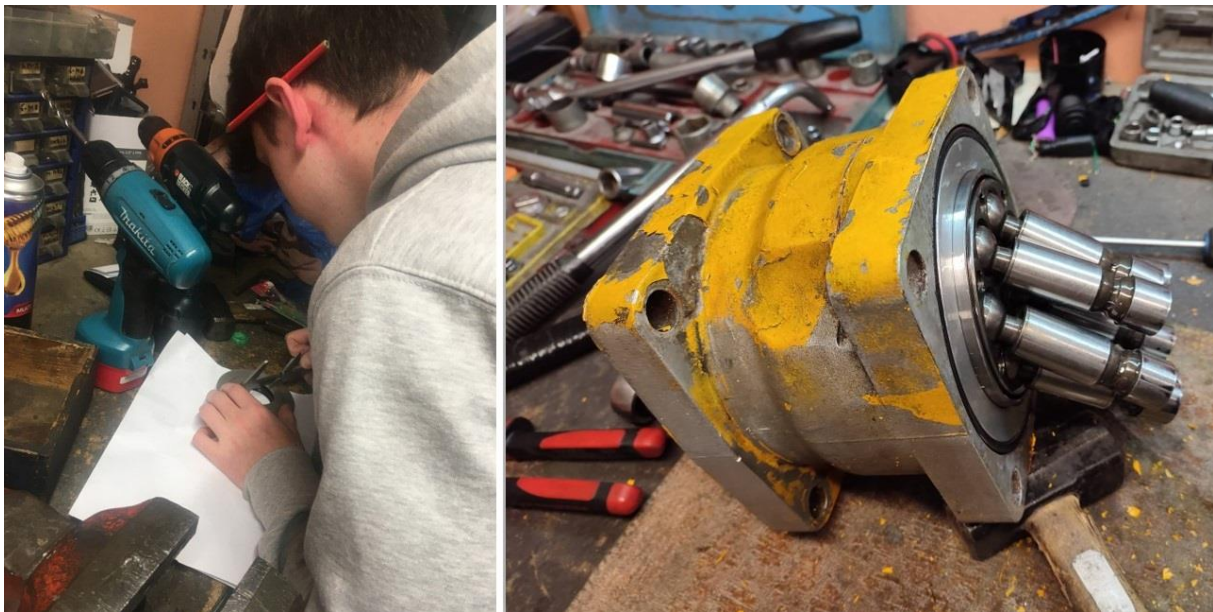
Hydraulický axiální pístový motor AMK 25-7 RS použitý v autojeřábu Tatra 815 AD 28
